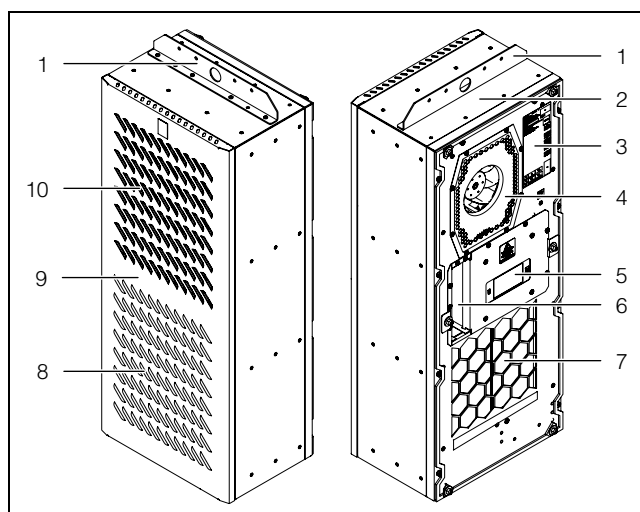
Principais componentes do condicionador de ar (SK 3185330)
